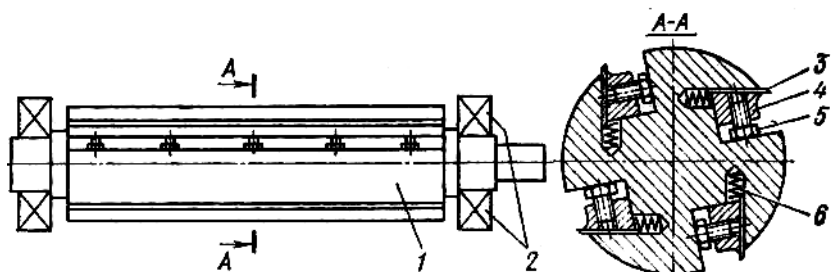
Ножевой вал фуговального станка СФК6-1: 1 — корпус, 2 — подшипники, 3 — нож, 4 — прижимный клин, 5 — винт, 6 — пружина
